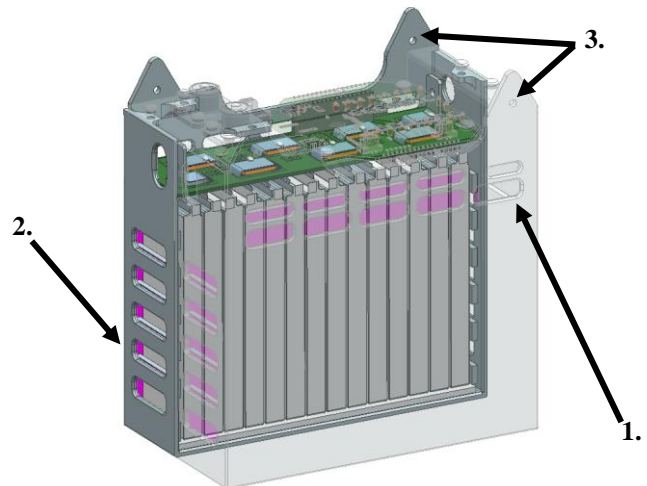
Zobrazenie peny (sivá farba) a pásky (ružová farba) na module
